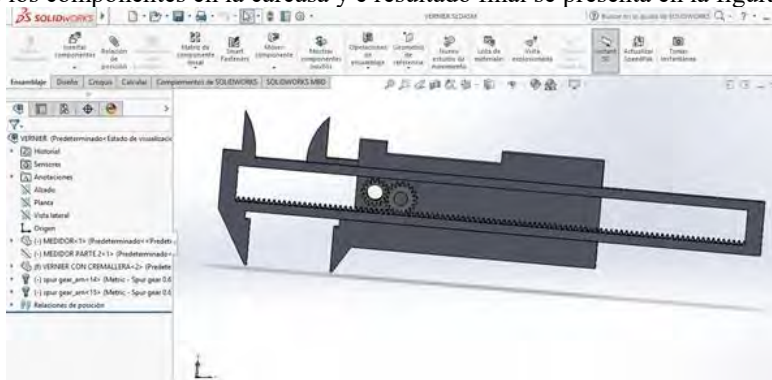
Carcasa del vernier digital inalámbrico diseñada en SolidWorks.
